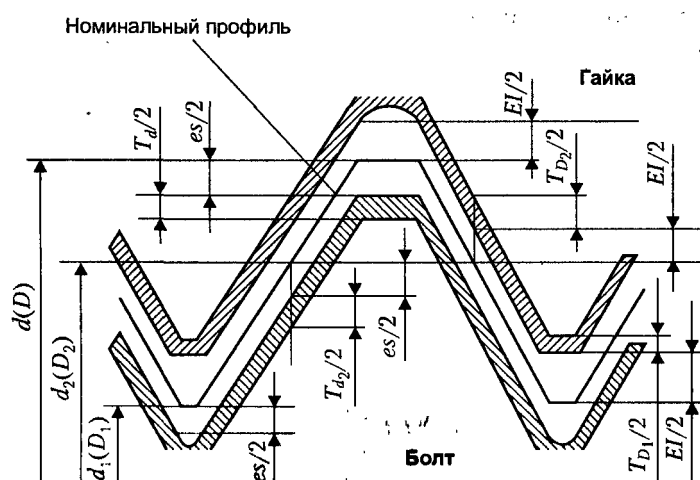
Расположение полей допусков метрической резьбы при посадке с зазором
